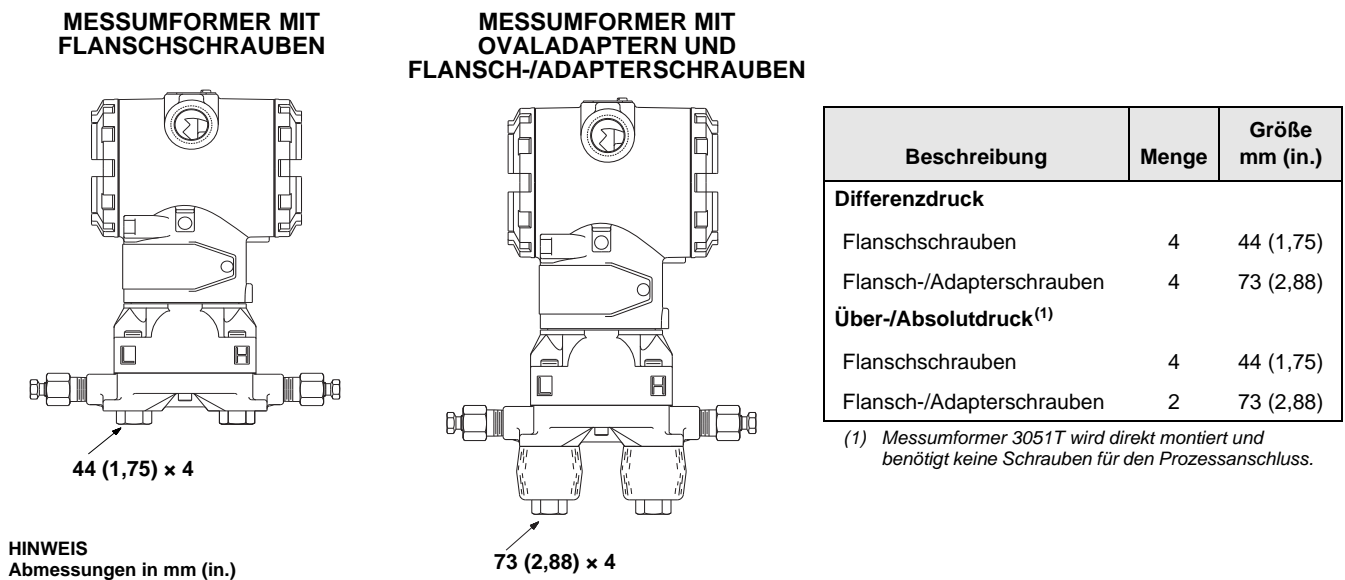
Montageschrauben und Schraubenkonfiguration für Coplanar Flansche
